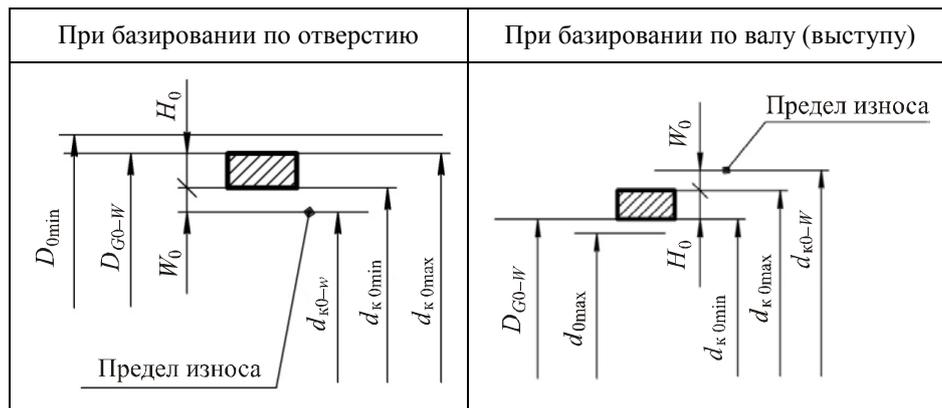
Схемы расположения полей допусков калибров без базовых измерительных элементов:
